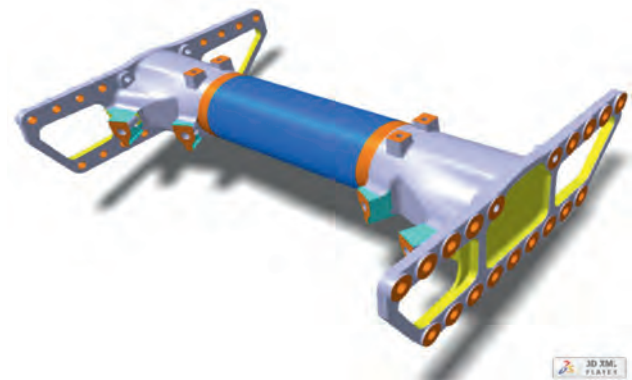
Rohrquerträger MagnetArc geschweißt
